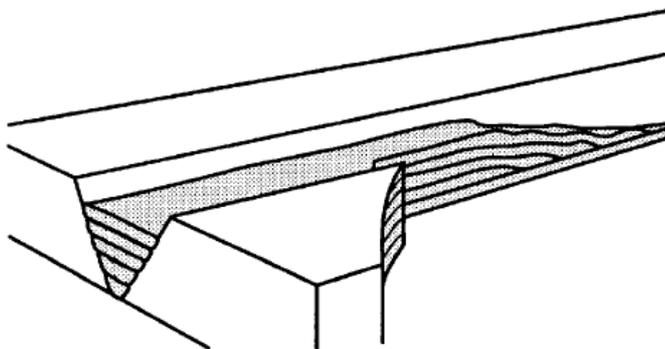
Secuencia en capas de la soldadura de cascada.
